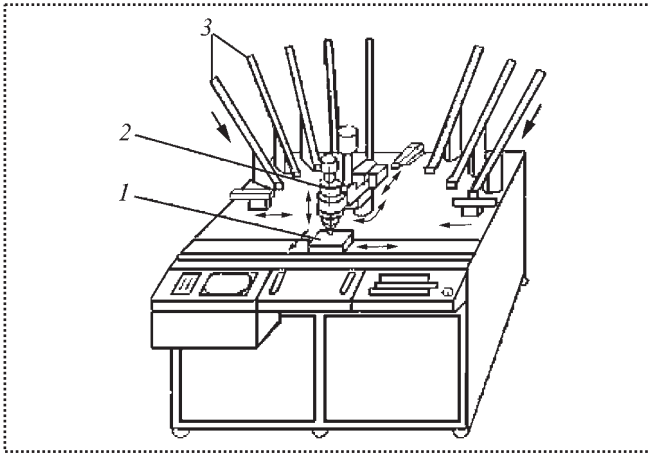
Роботизированный комплекс для монтажа корпусных ИМС со штырьковыми контактными выводами на печатную плату:
